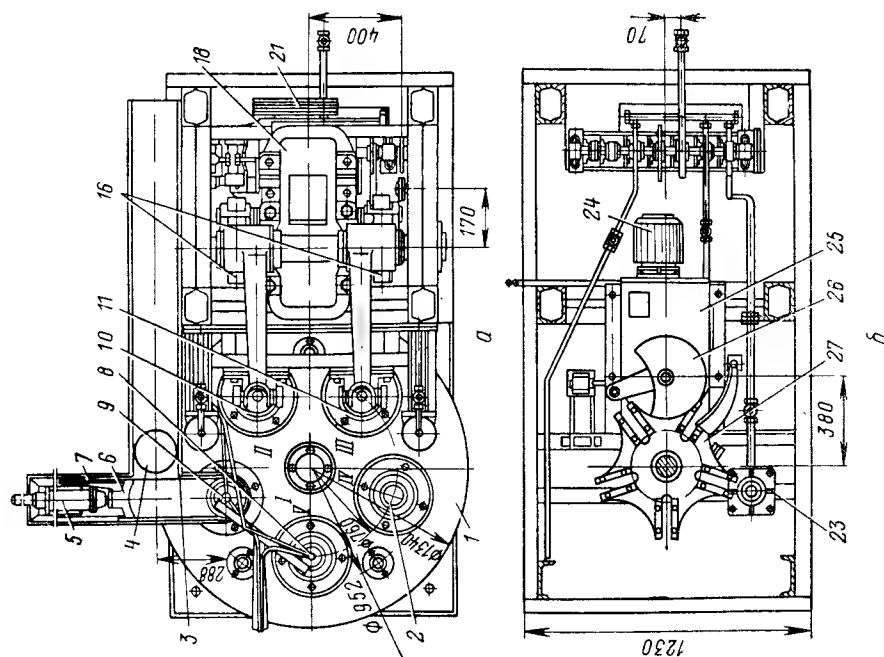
Схема автомата для формирования конусообразных заготовок:
